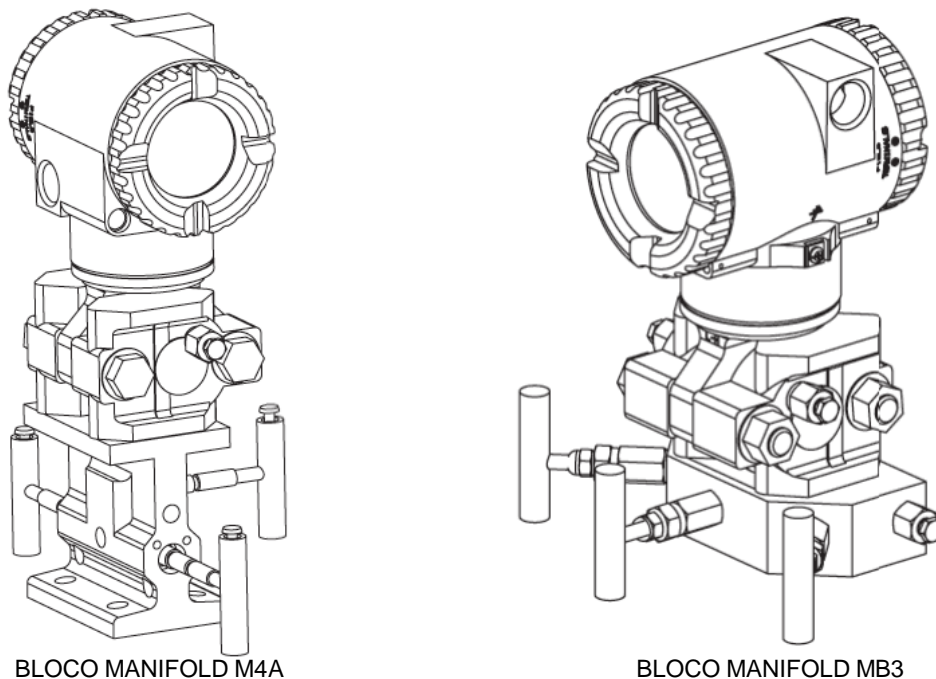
Montagem Típica do Transmissor IDP com suporte pelo bloco manifold tipo bypass
